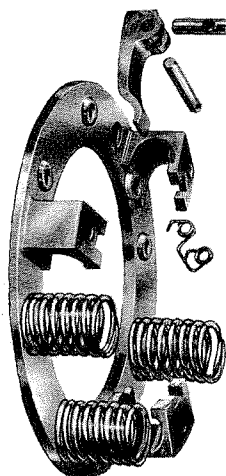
A Plato de presión accionado por resortes helicoidales.
